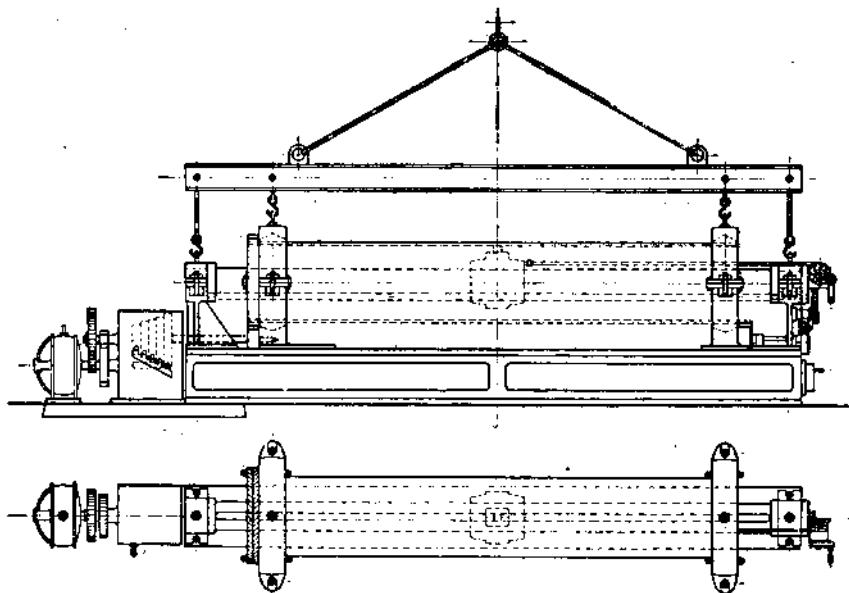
Станок для расточки длинных цилиндров с вращающимся изделием.
